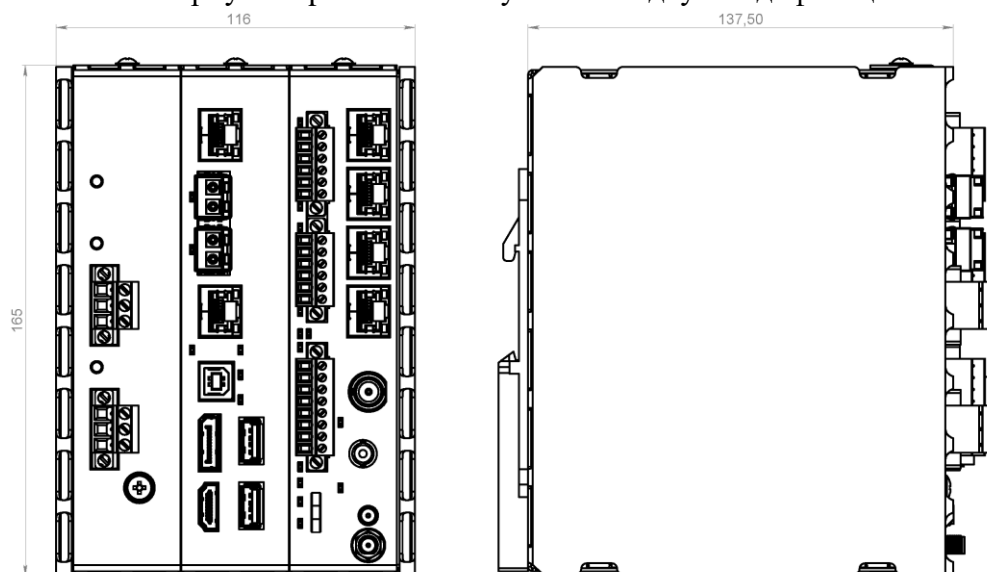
Внешний вид и габаритные размеры - корпус (ШхВхГ) 120 x 180 x 170 мм.
